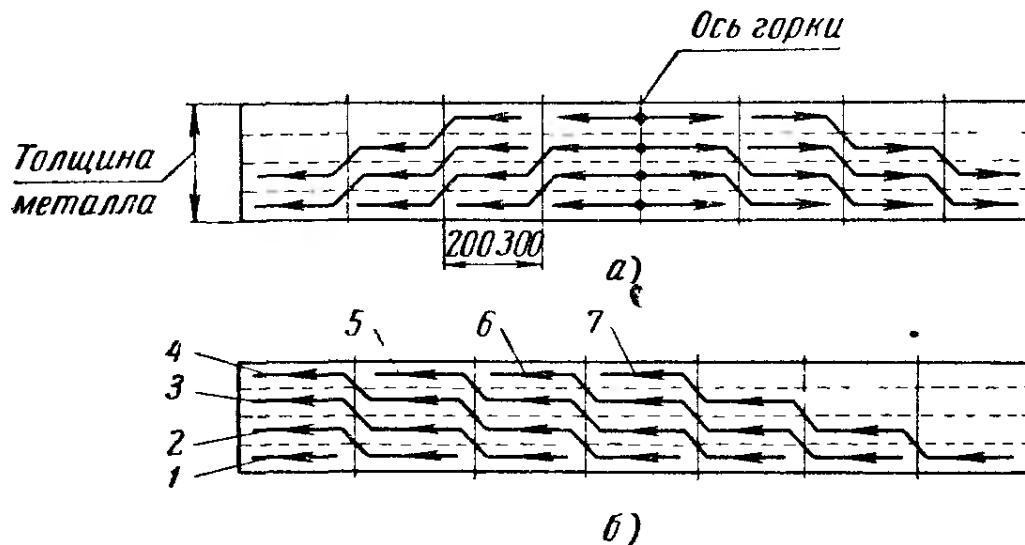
Последовательность наложения швов при многослойной сварке:
